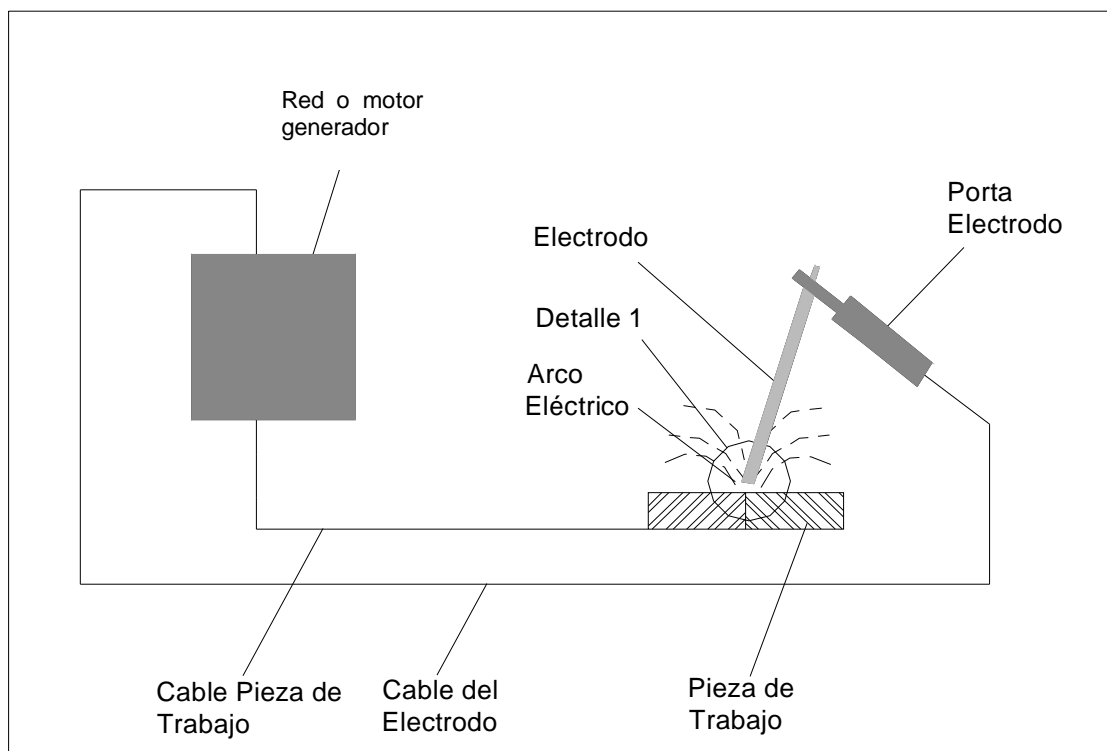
a). – Elementos de un circuito de soldadura típico para soldadura por arco de metal protegido. (THE PRODUCE HANDBOOK OF ARC WELDING, sección 1, Pág. 1. 3 – 1)
